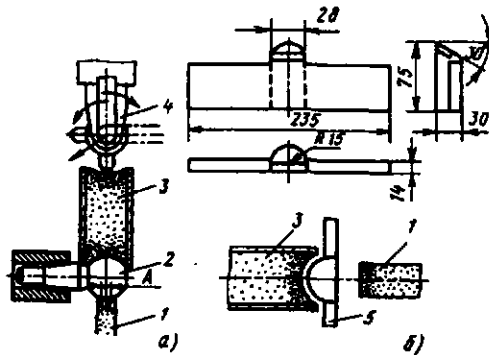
Схема наладки для шлифования сферы шарового пальца: а – схема расположения кругов и профильной правки режущей поверхности; б – опорный нож для шлифования шаровой поверхности
